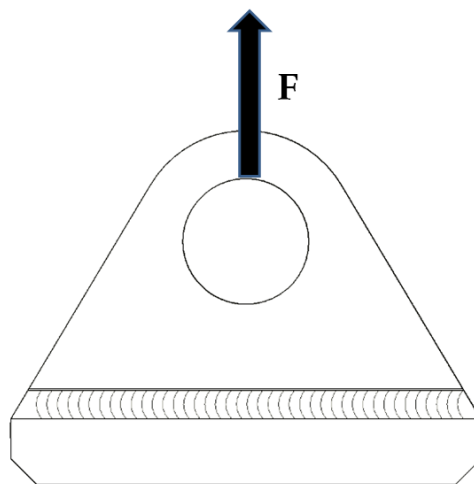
22 Fuerza transmitida a la soldadura
